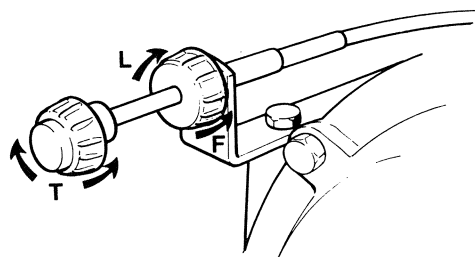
Commande du régime moteur à partir de la chambre des machines
